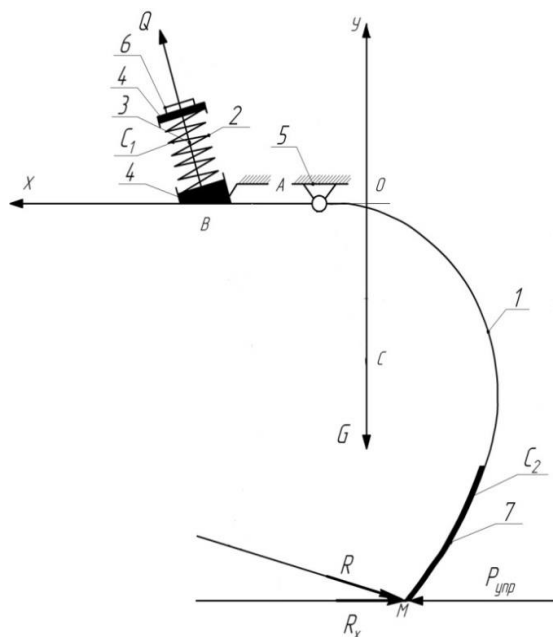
Схема конструкции стойки чизель - культиватора с шарнирно-упругим креплением к раме:
